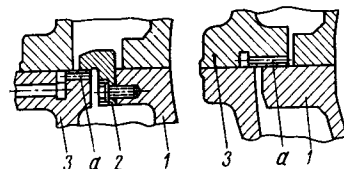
Соединение внешнего корпуса турбины ГТ-12-3 ЛМЗ с внутренним при помощи опорных лап: а — отверстие; 1 — внутренний корпус; 2 — монтажная лапа; 3 — внешний корпус
